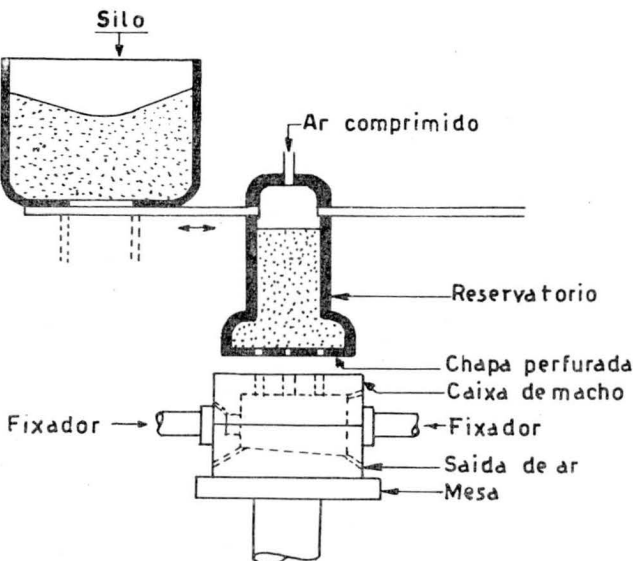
Esquema de conjunto de uma máquina de soprar machos.
